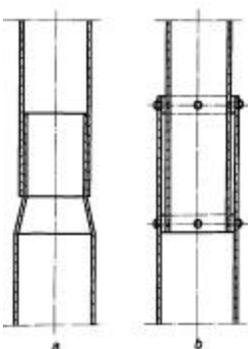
Juntas para postes tubulares de acero. a- Junta cónica. b- Junta cilíndrica
